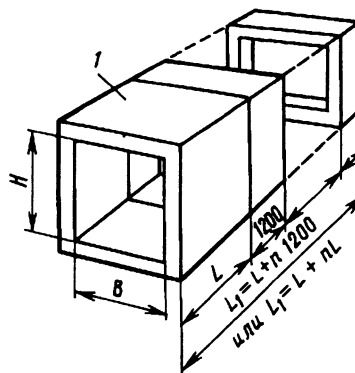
Схема компоновки универсальных прямоугольных сварочных вакуумных камер из модулей I
